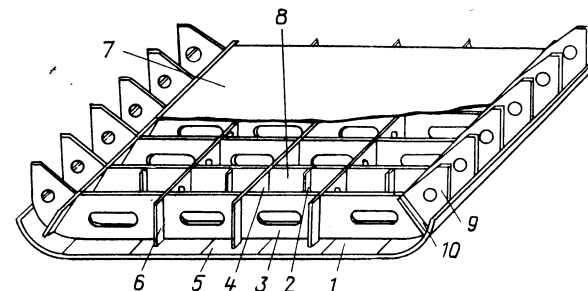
Конструкция днищевых перекрытий с двойным дном при поперечной системе набора
